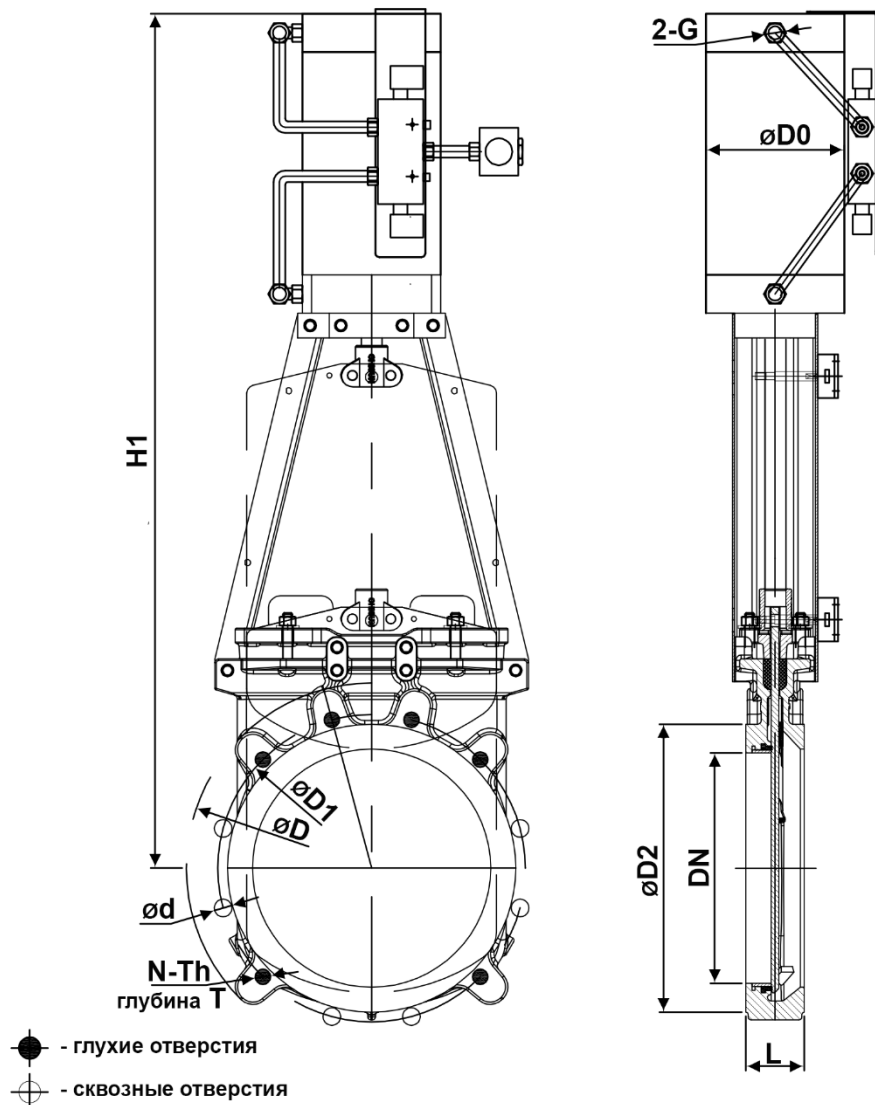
Размеры задвижки в сборе с пневмоцилиндром
